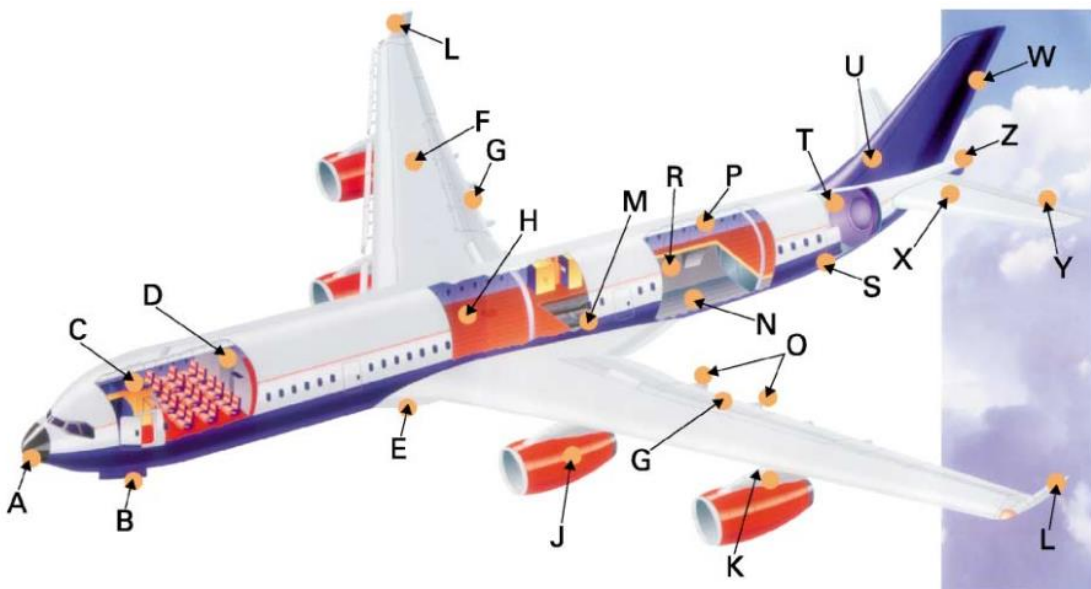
Esquema genérico de aplicação de ligações adesivas na construção da estrutura de um avião comercial [10].
